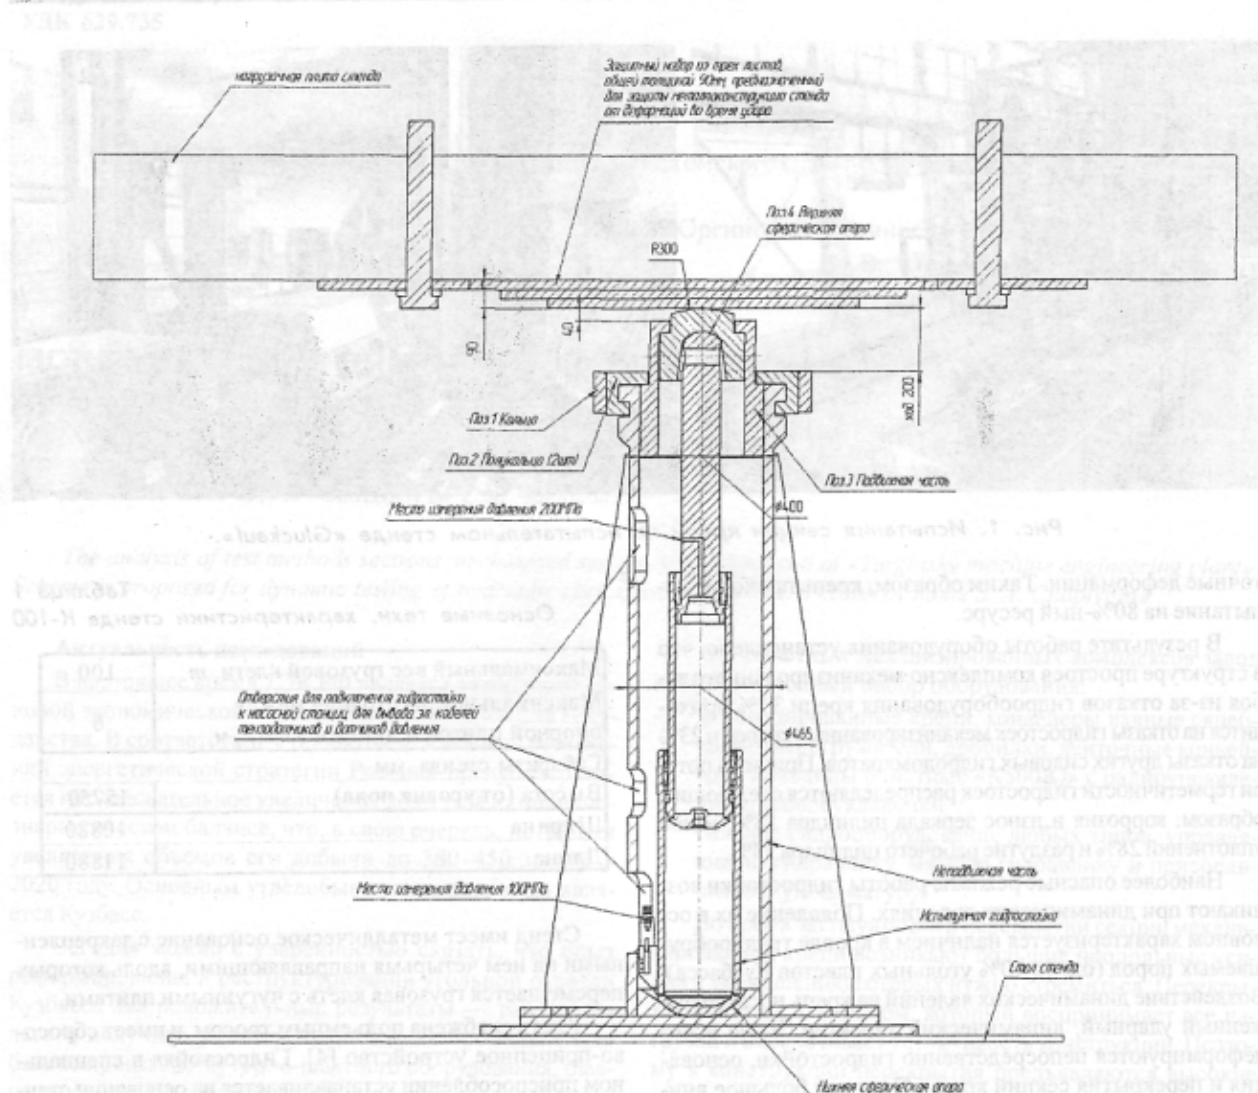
Схема динамических испытаний гидростойки на станде К-100.
